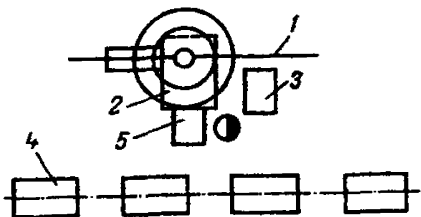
Схема планировки рабочего места при изготовлении стержней на пескоструйной машине модели С-216: 1 — монорельс для подачи стержневой смеси; 2 — пескоструйная машина; 3 — этажерка для хранения сушильных плит (драйверов); 4 — подвесной конвейер с этажерками; 5 — приставной стол
